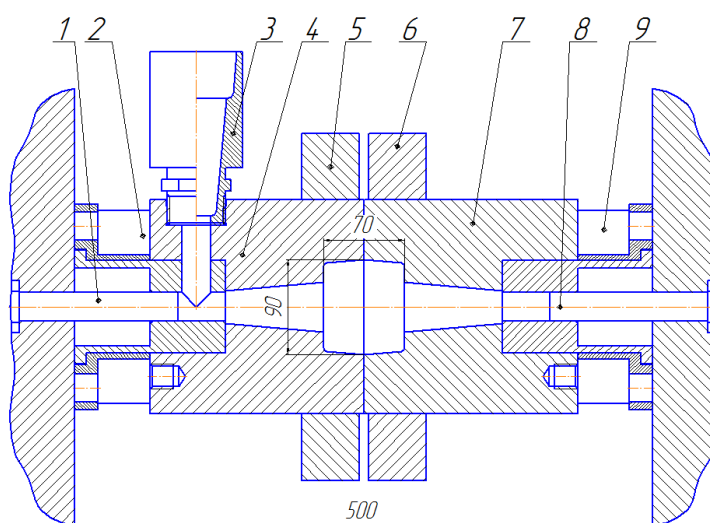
б. Чертеж технологической оснастки для производства заготовок поршей ДВС
